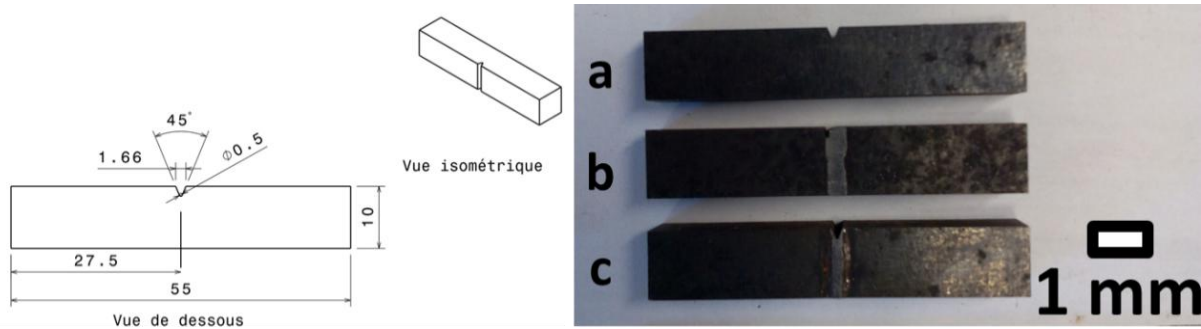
Plan des éprouvettes Charpy normalisées à gauche et vue de dessus des éprouvettes Charpy après usinage à droite : (a) Métal de base, (b) Zone affectée thermiquement, (c) Zone de fusion
